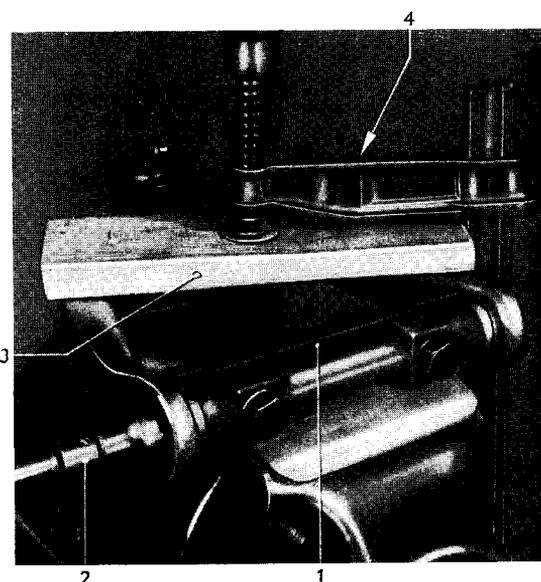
Lenker zum Einschrauben der Gewindebuchsen festgespannt
